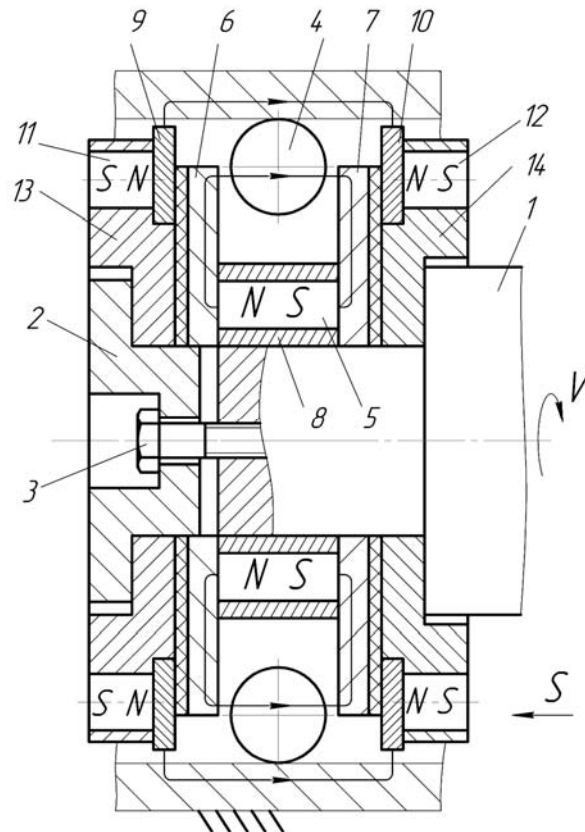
Схема реализации комбинированного магнитно-центробежного накатывания с дополнительным намагничиванием поверхности детали
